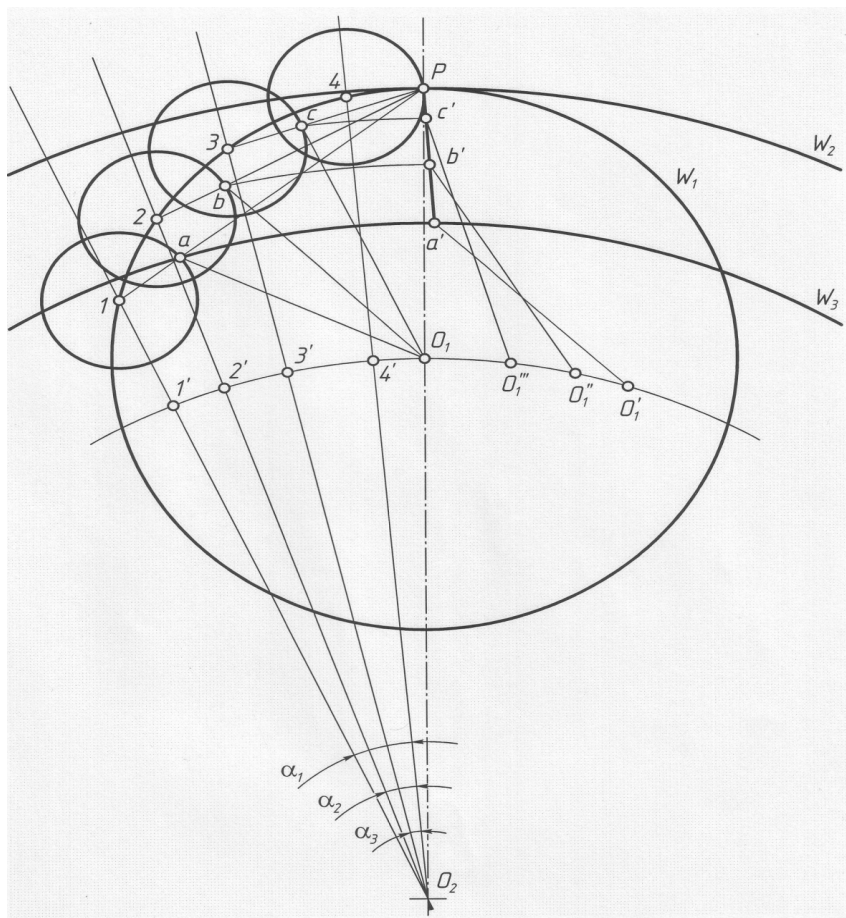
Схема построения профиля зуба колеса при зубе шестерни, имеющем форму тела вращения.
